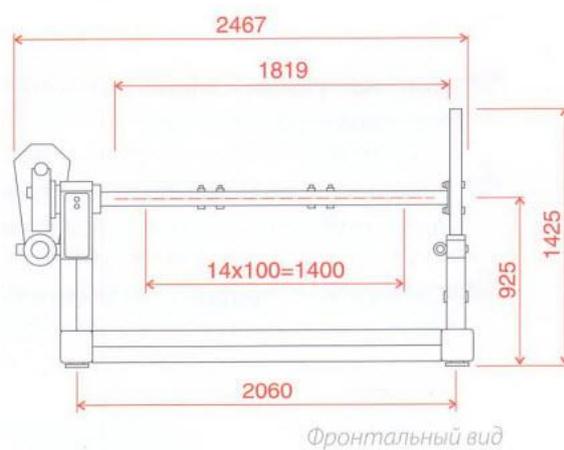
Стенд Р-770Е (габаритные размеры)
